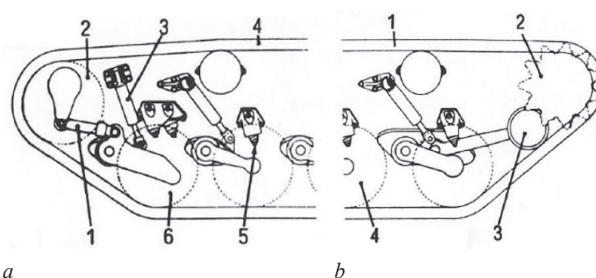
Способы регулирования силы предварительного натяжения: а: 1 — баланси́р с устройством натяжения цепи; 2 — ленивец (натяжное колесо); 3 — амортизатор; 4 — гусеничная цепь; 5 — упор; 6 — опорный каток; б: 1 — гусеничная цепь; 2 — ведущее колесо (звездочка); 3 — натяжной ролик; 4 — опорный каток
